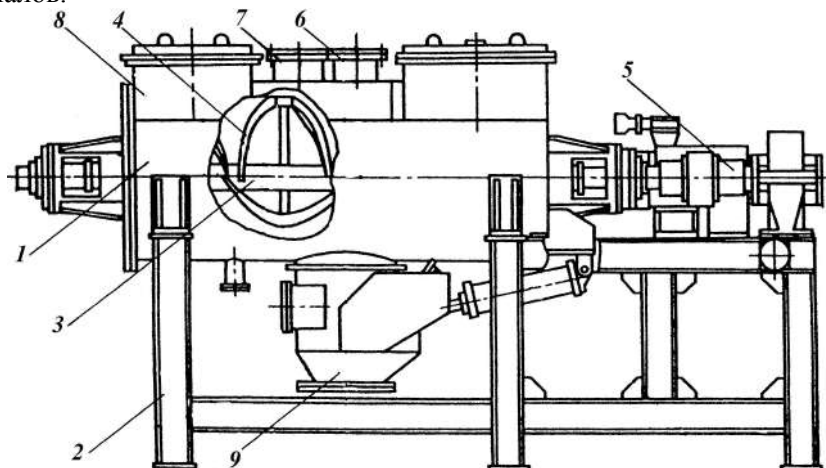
Смеситель ленточный типа Лн: 1 – корпус; 2 – рама; 3 – ротор; 4 – лента; 5 – привод; 6, 7 – штуцер; 8 – люк; 9 – разгрузочный люк.
